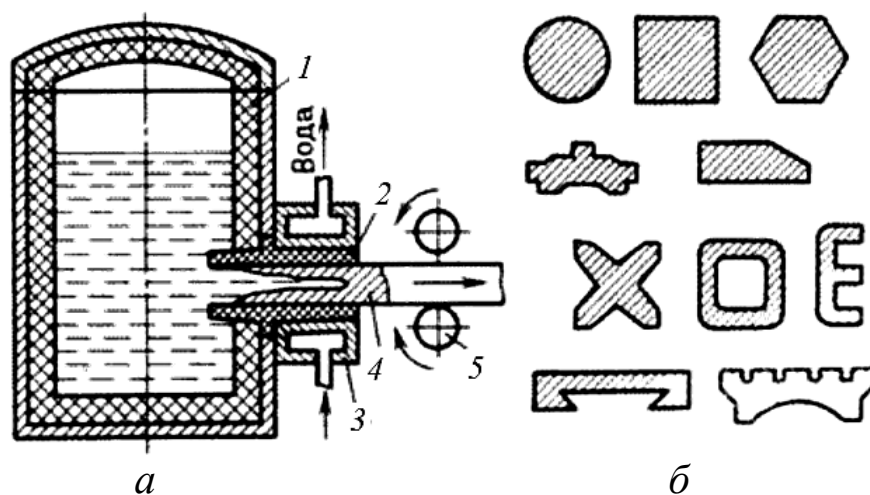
Схема непрерывного литья (а) и разновидности получаемых отливок (б)
